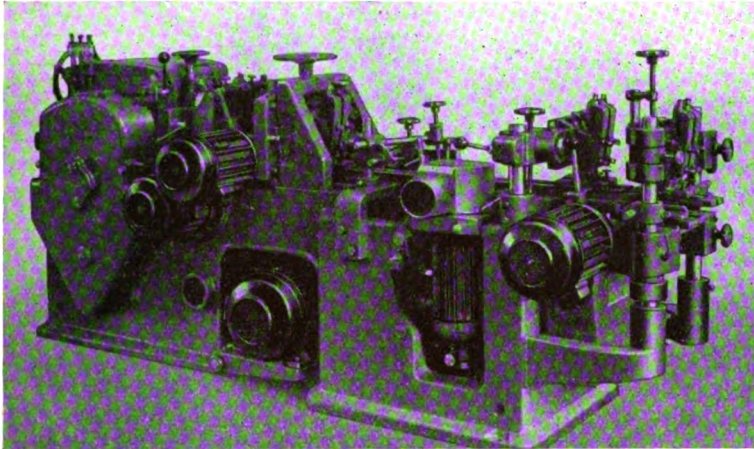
Elektro-Hobelmaschine für Fußbodenbretter.
